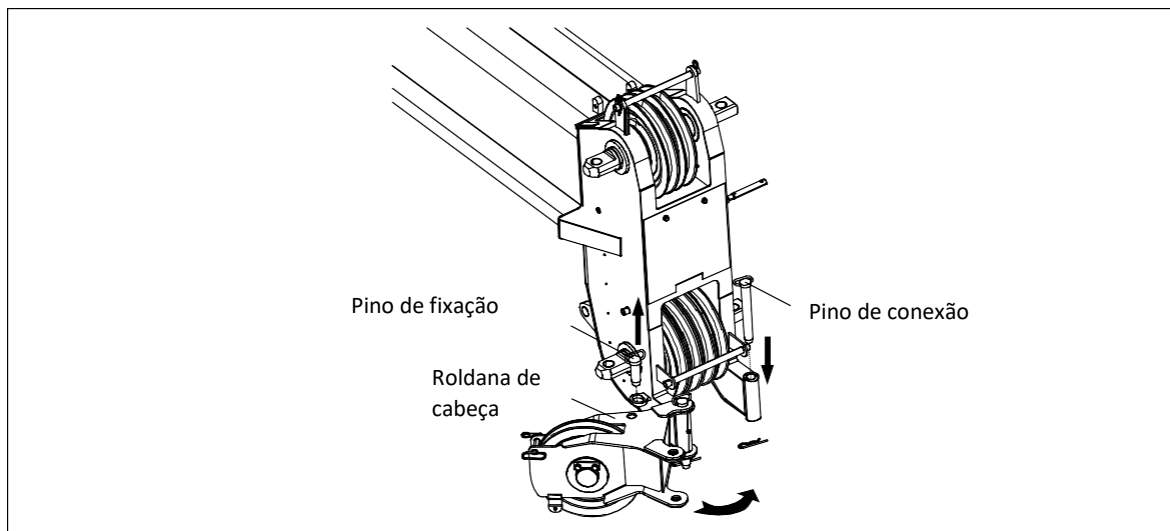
CONJUNTO DA ROLDANA DE IÇAMENTO AUXILIAR
